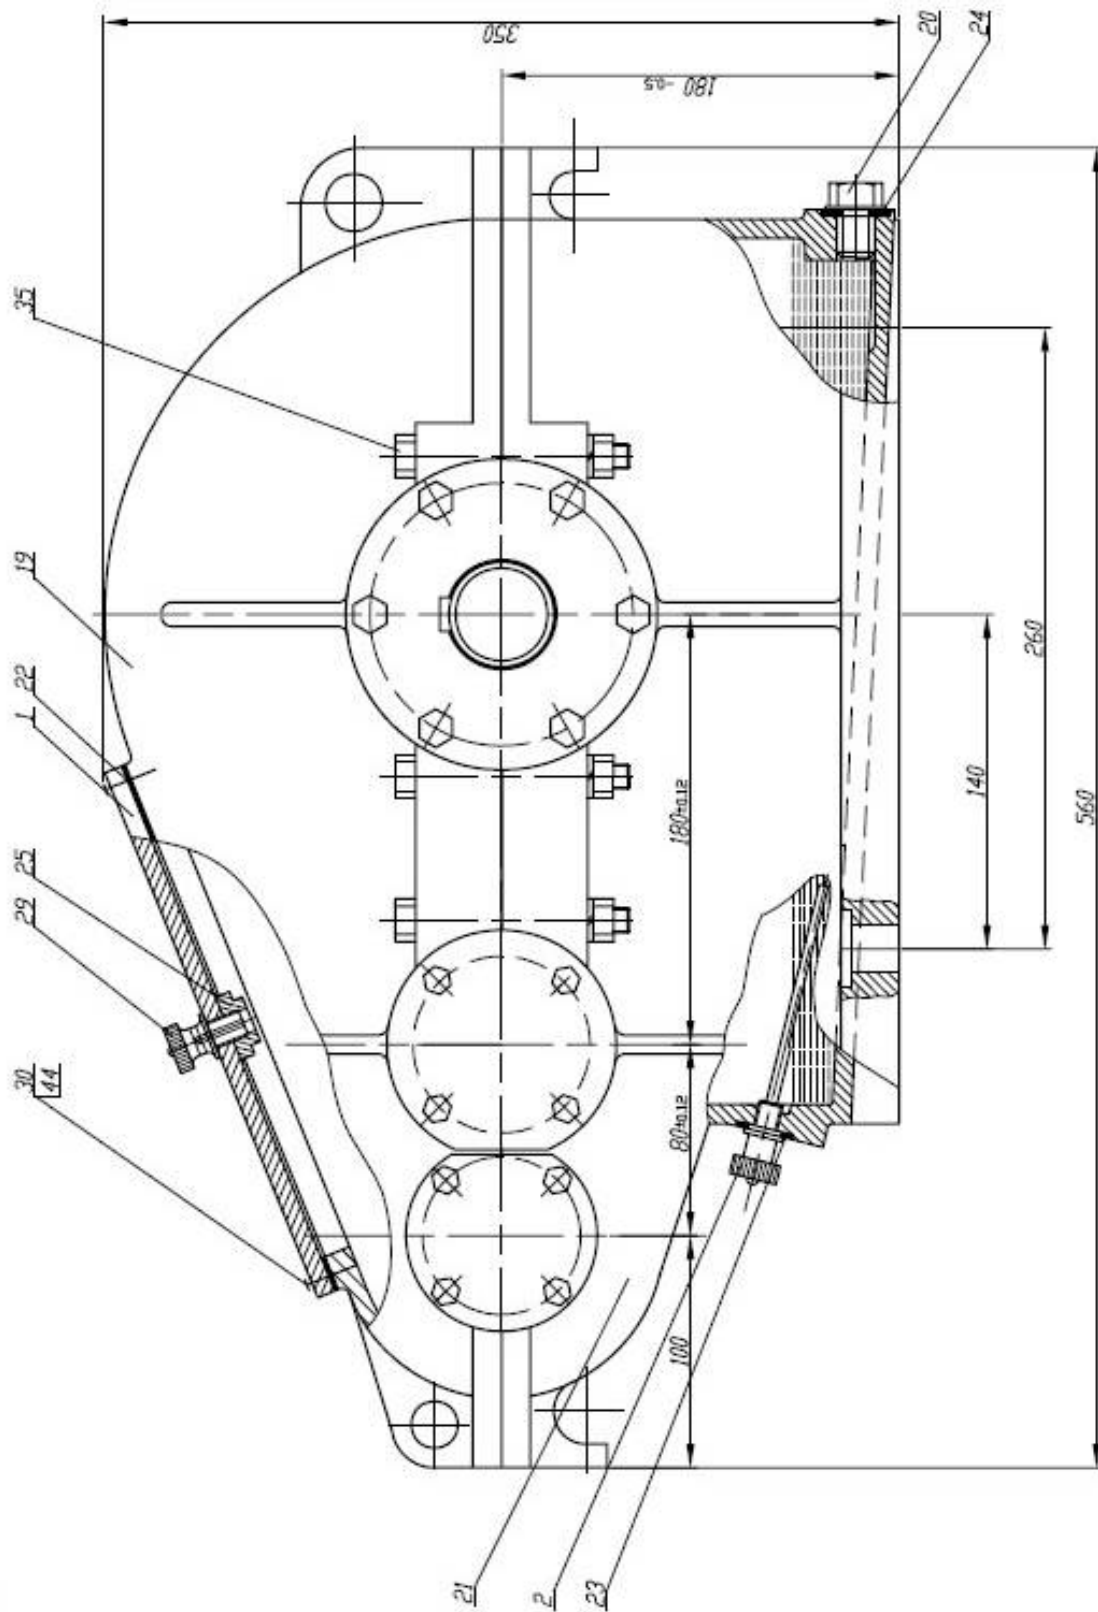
Укрупненный вид редуктора спереди на рисунке К.1
